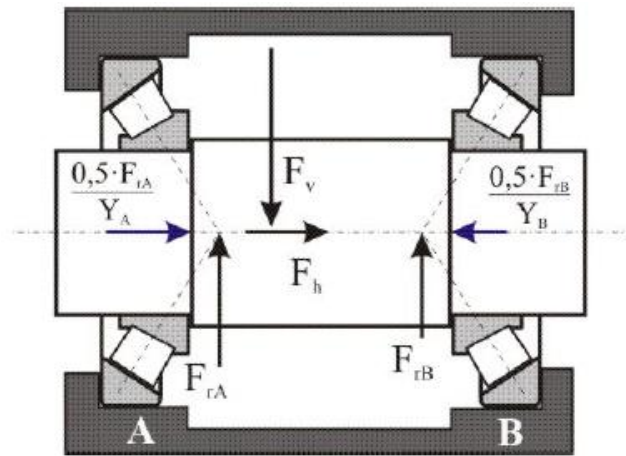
Fuerzas en rodamientos de rodillos cónicos
